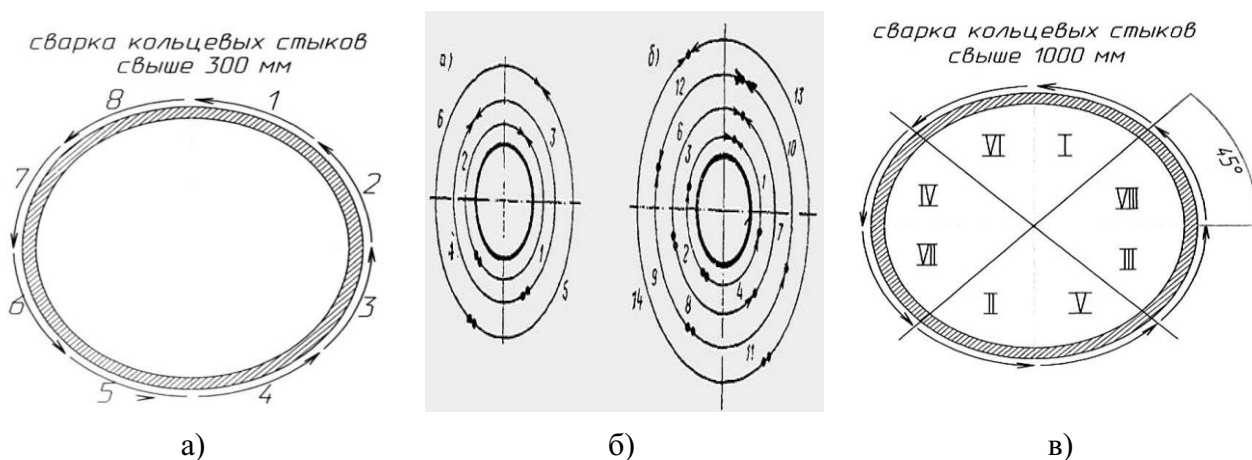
Схемы основных методов сварки на предлагаемой установке: обратноступенчатый способ (а), многослойная сварка (б) и сварка крест-накрест (в)
